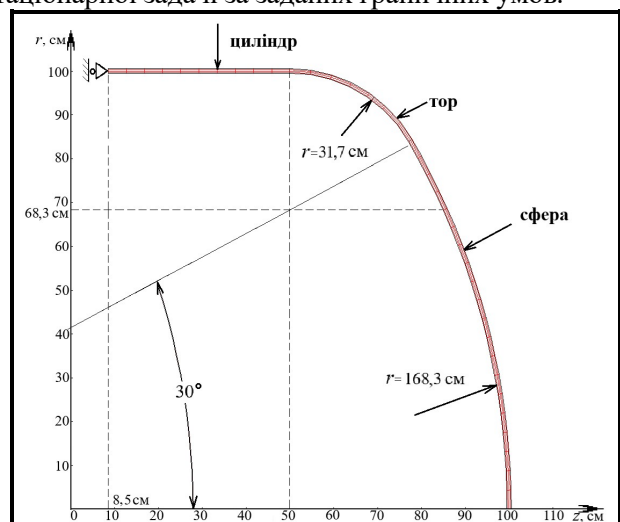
Осесиметрична розрахункова схема половини звареної заготовки посудини
